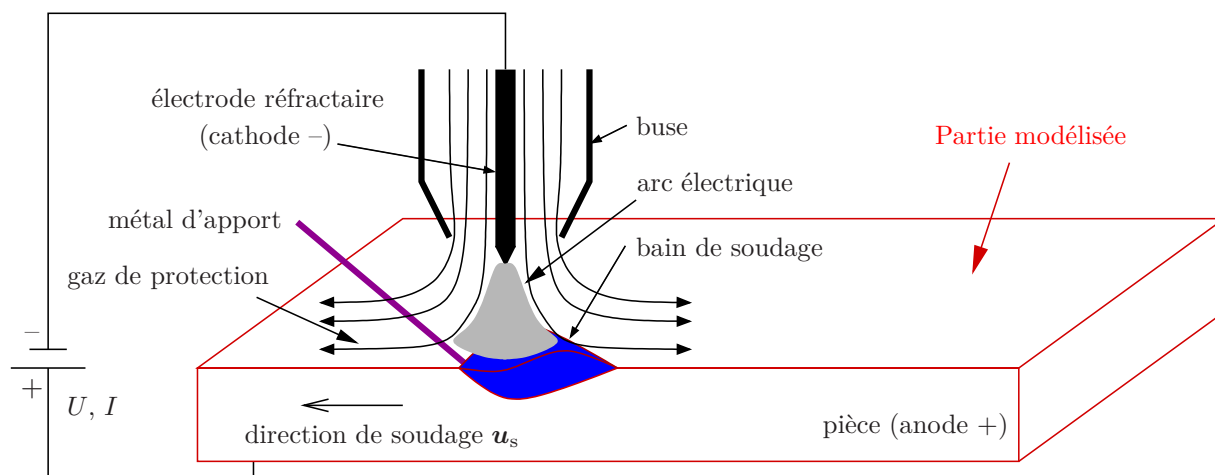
Schéma plaque et bain de soudage (partie rouge) du procédé à l'arc TIG.
